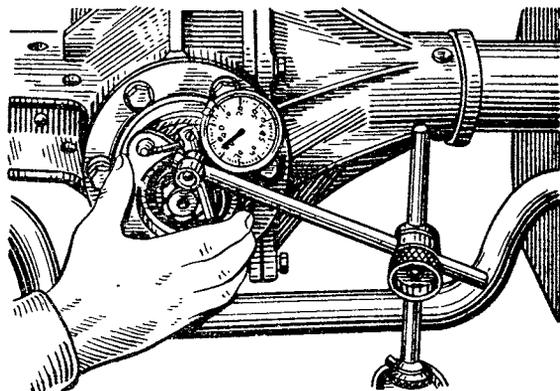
Определение бокового зазора в зубьях ведущей и ведомой шестерен
